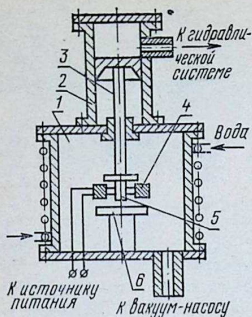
Принципиальная схема установки для диффузионной сварки в вакууме:
